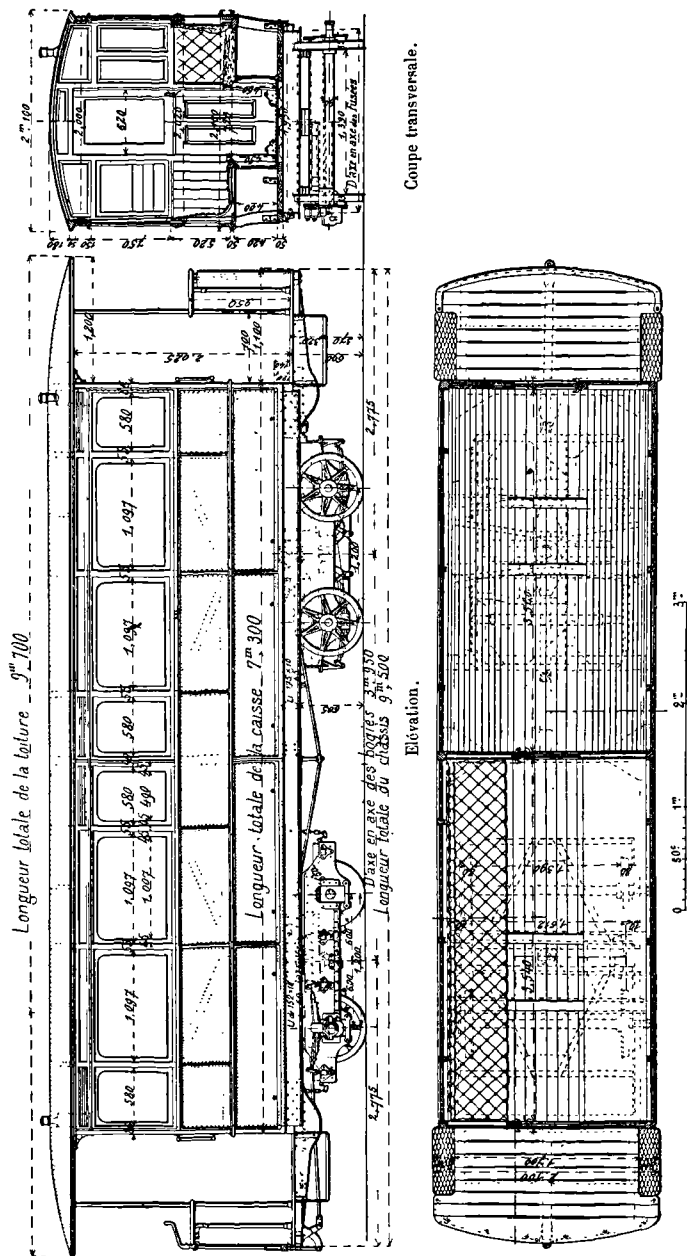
Projet d'automobile à bogies de la Société Franco-Belge.
